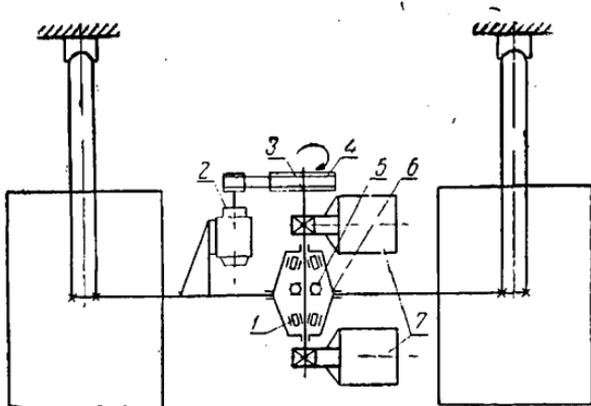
Кинематическая схема безверетенного самобалансирующего привода рассева.
